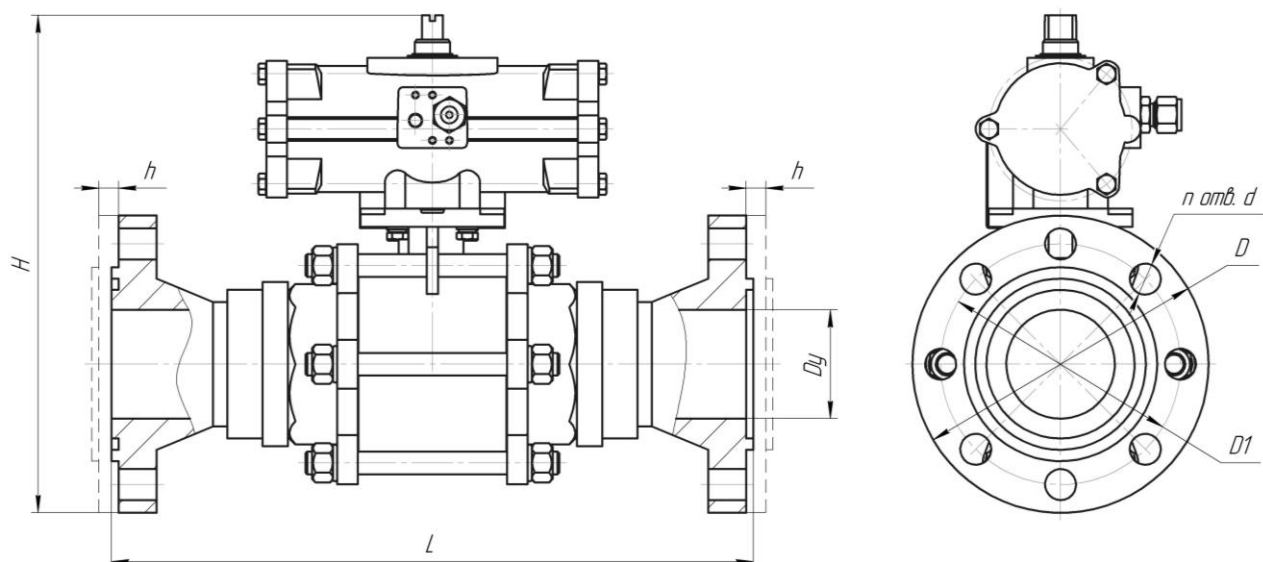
Габаритный чертеж устройства РУС-III с приводом из нержавеющей стали без пускового узла
